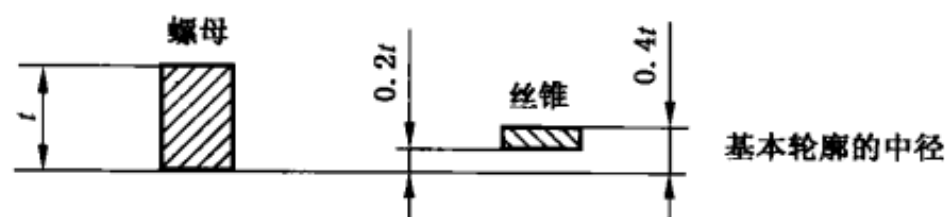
G 螺纹丝锥的螺纹中径公差带
